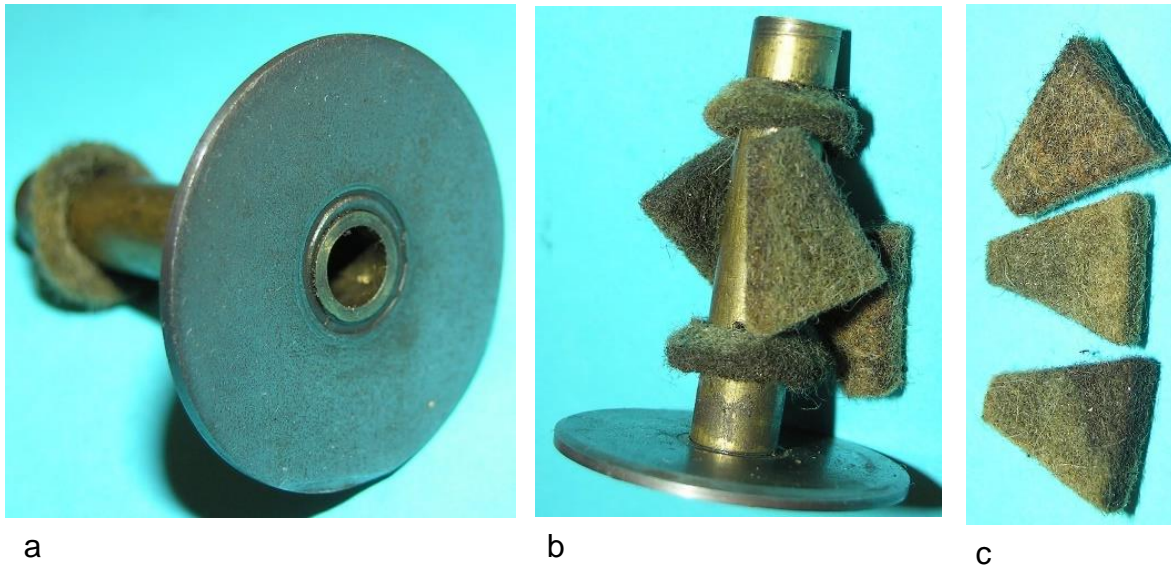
Gleitlager: a) Lagerschild mit Lagerrohr, b) Filzelemente im Lagerraum, c) Einlegeteil
